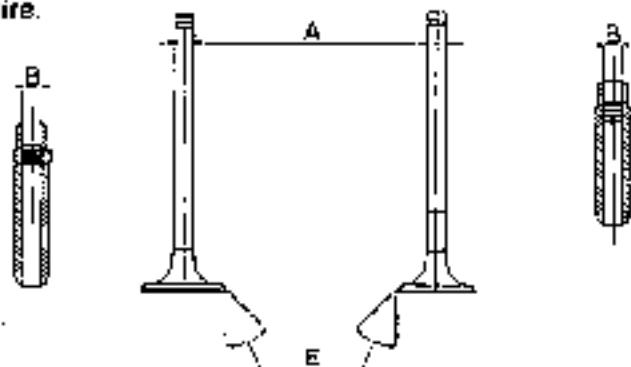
Dimensioni principali delle valvole e delle guide valvole
